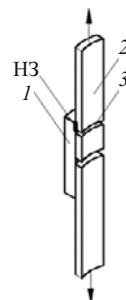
Эскиз образца сварного раструбного соединения на растяжение
